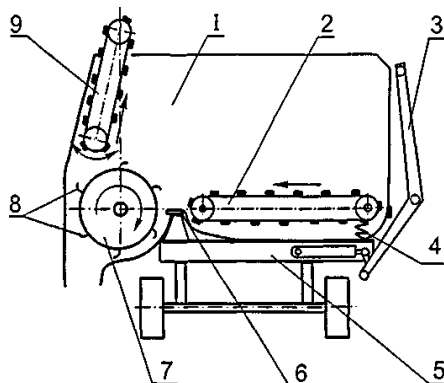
Конструктивно-технологическая схема измельчителя-раздатчика грубых кормов:
